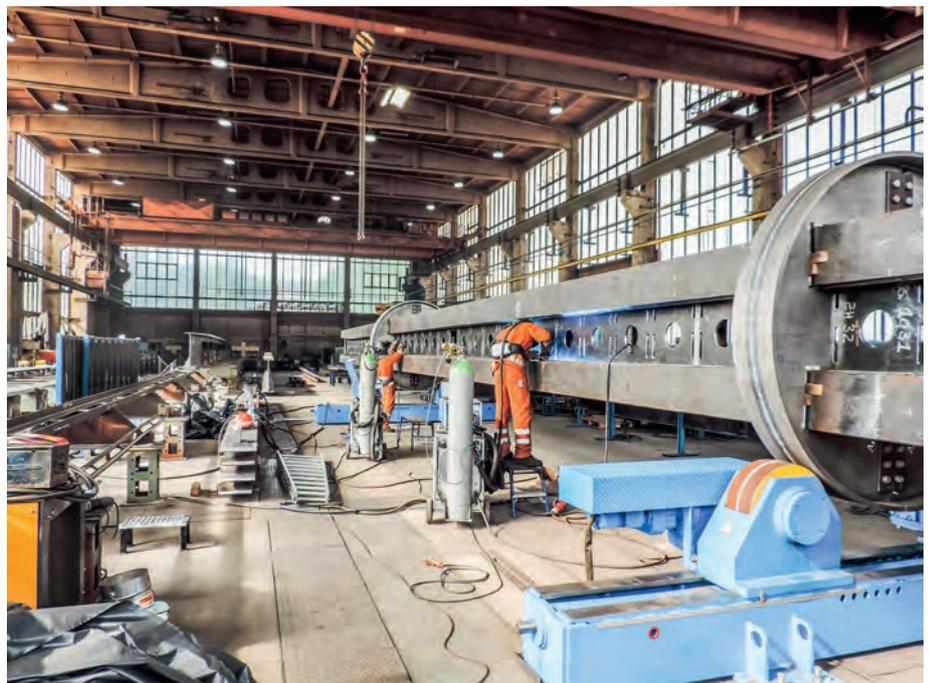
Zwillingsträger in Drehvorrichtung beim Schweißen der Fahrbahnblechlängsnaht
